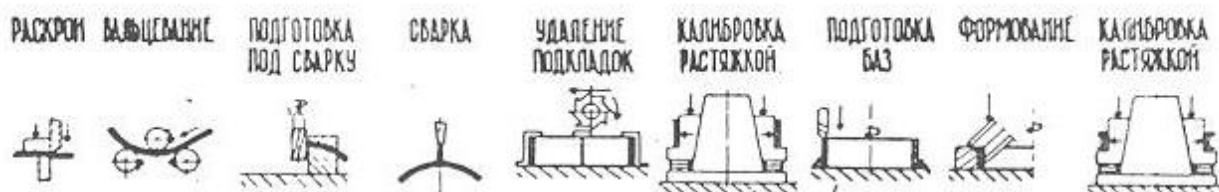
Технологическая схема получения колец формовкой из листовой заготовки
